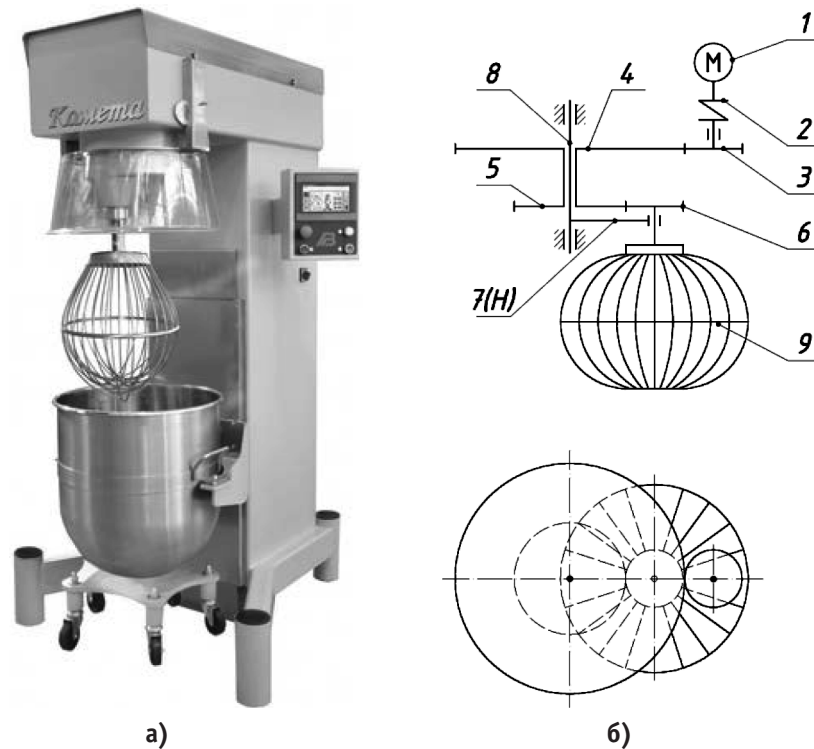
Промышленная установка планетарного миксера (а) и кинематическая схема (б) односателлитного планетарного миксера, где: 1 — электродвигатель, 2 — муфта, 3 — шестерня, 4 — простое зубчатое колесо, 5 — солнечное колесо, 6 — спутник, 7 (Н) — водило, 8 — вал, 9 — месильный орган венчика сжатого эллипсоидального вращения
